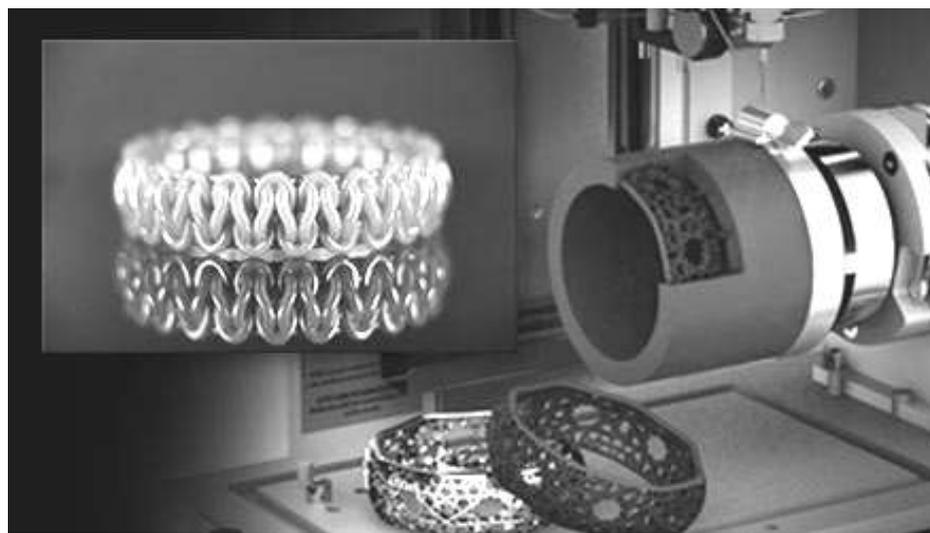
Фрагмент гравировально-фрезерного станка с ЧПУ Revo540CX
